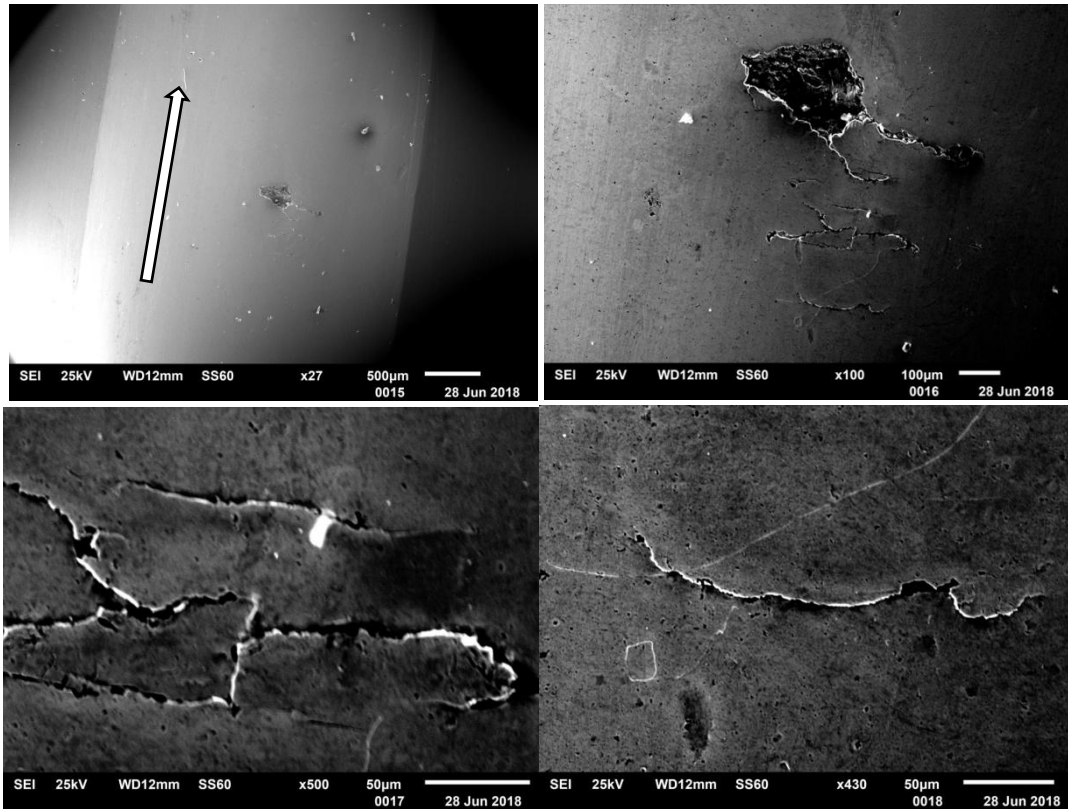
Изображение питтинга на поверхности дорожки качения подшипника. Стрелка указывает направление качения кольца.
